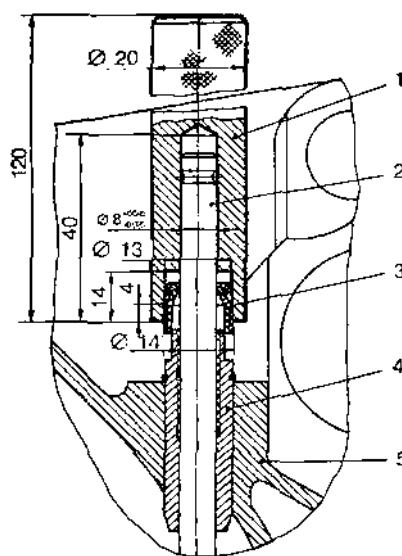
Оправка для запрессовки маслоотражательного колпачка клапана:
